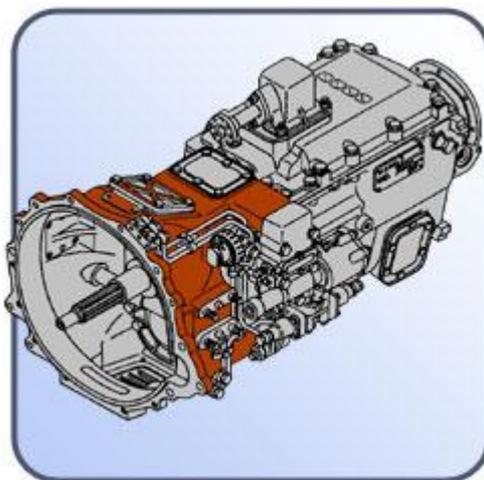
Коробка передач автомобиля КамаАЗ
